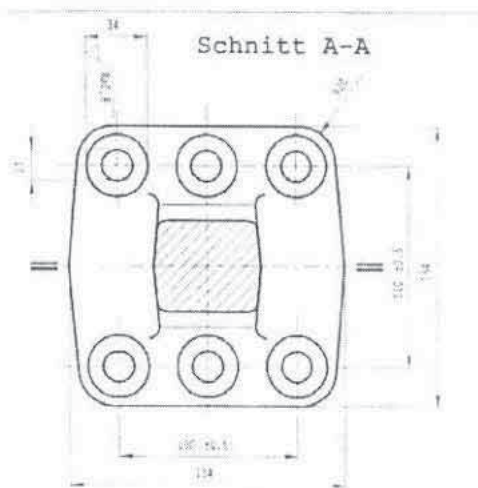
Zugöse Ausführung 1 mit 6 Loch Flanschbefestigung
